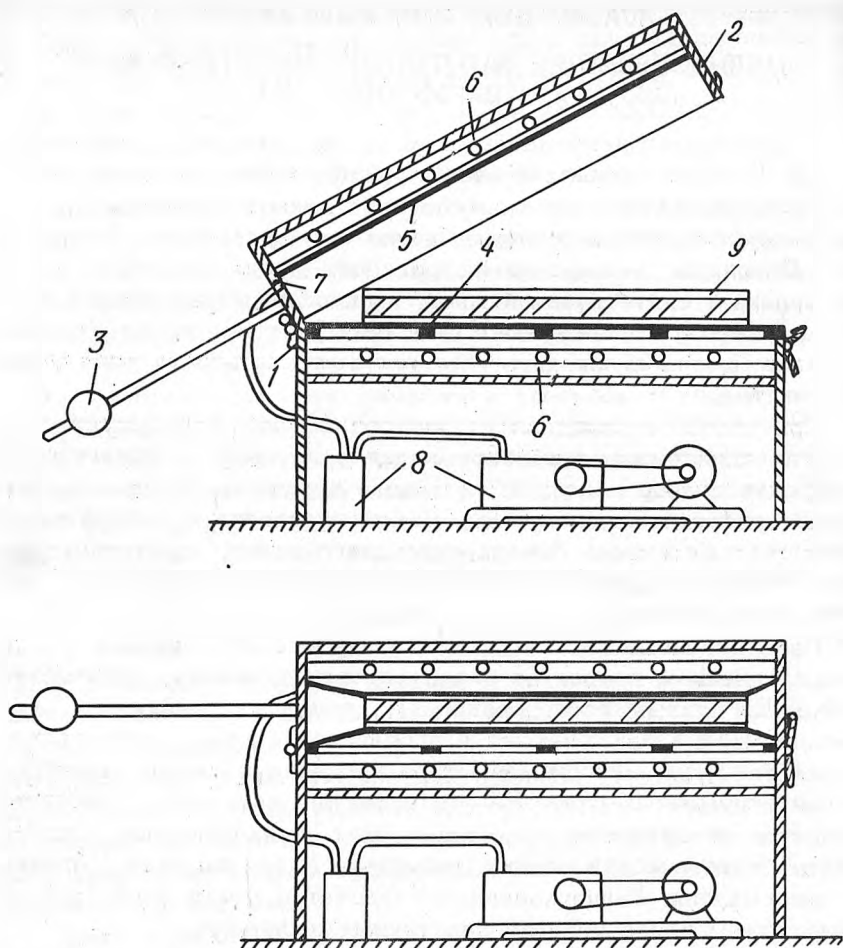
Схема вакуумного процесса для двустороннего облицовывания заготовок:
